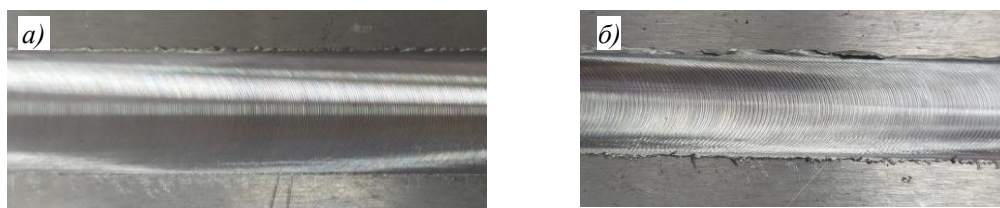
Внешний вид сварных соединений из сплавов В-1213 (а) и 1151 (б), выполненных сваркой трением с перемешиванием
